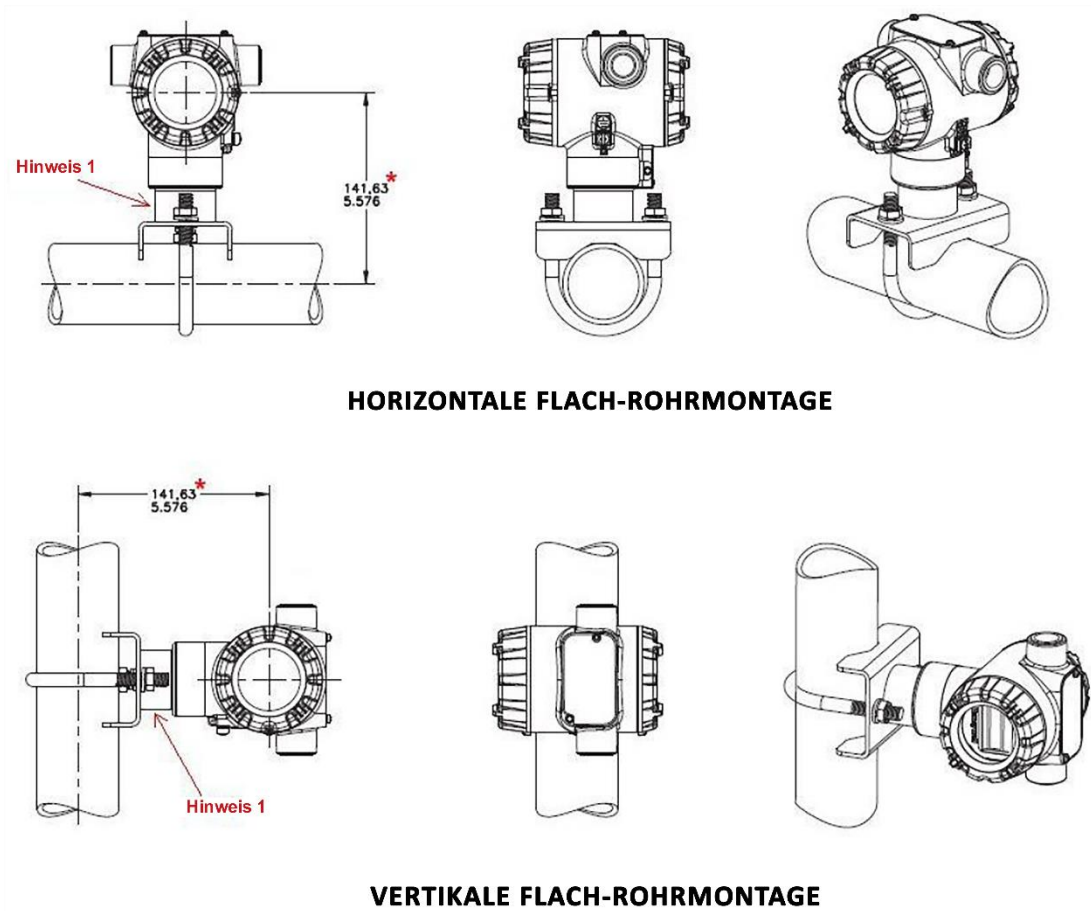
STT750 Rohrmontage mit Adaptergehäuse – Horizontal und Vertikal
